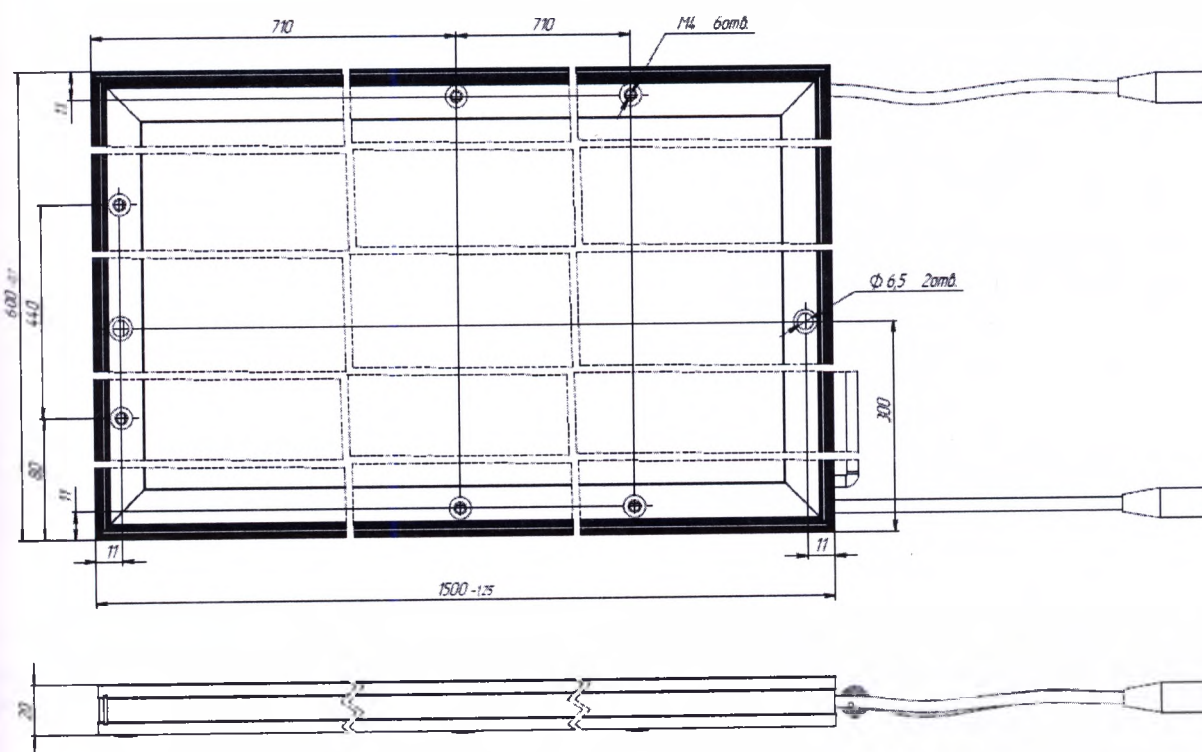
б – Габаритные и присоединительные размеры сегмента подсветки буферного блока Lat-1
